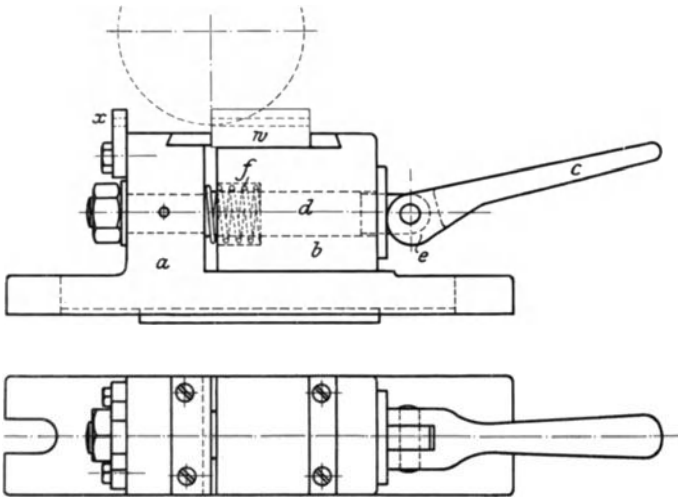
und 181. Durch Hebeldruck spannende Fräsvorrichtung.
